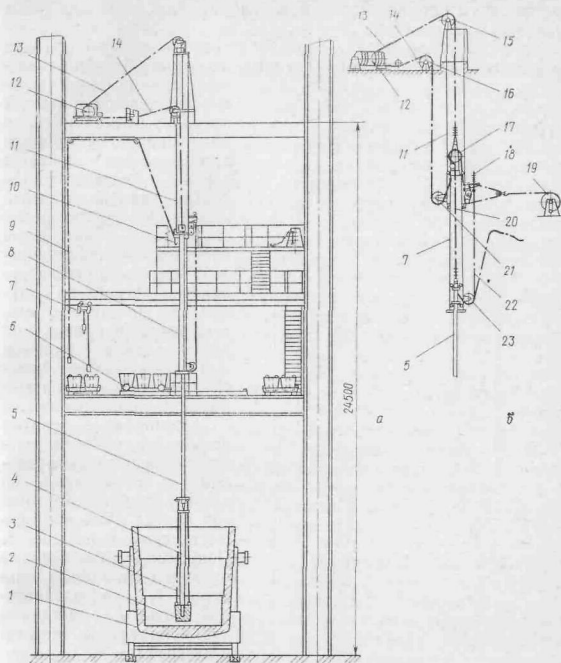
Машина для ввода алюминия в сталеразливочный ковш
